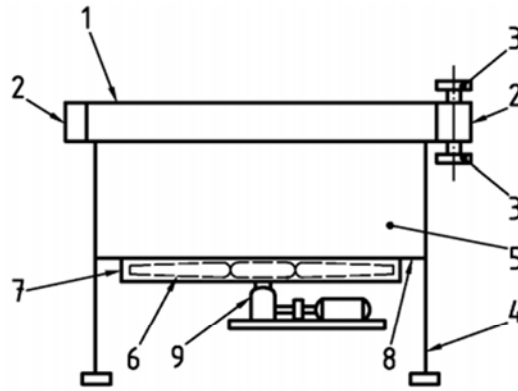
Cabina del conjunto turbocompresor y equipo auxiliar
